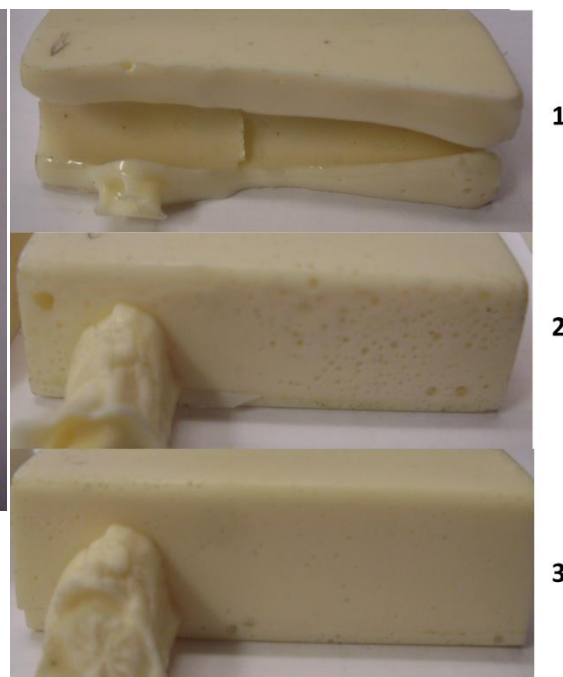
Viditelné vady způsobené při odlévání součástí.
